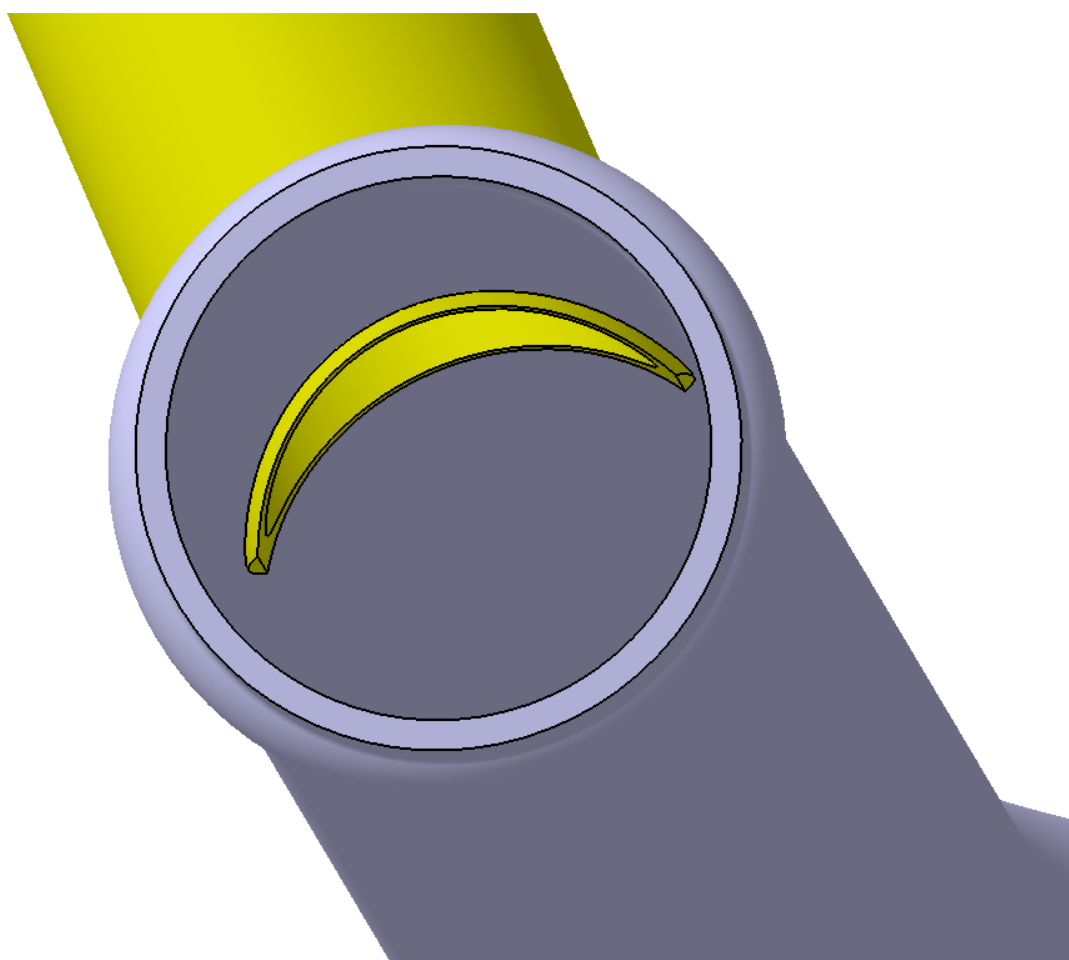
Фрезеровка торца трубы отводящей радиатора отопителя
